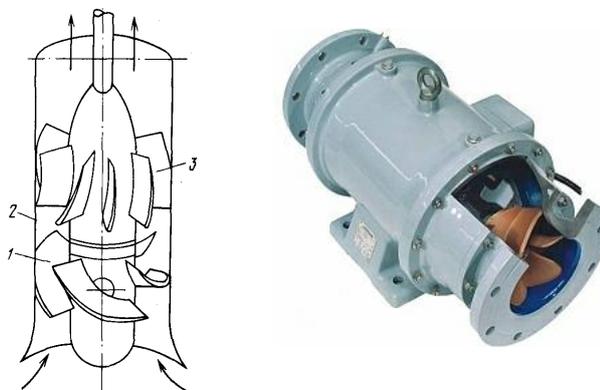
Осевой насос: 1- рабочее колесо; 2 - корпус; 3 - направляющий аппарат
